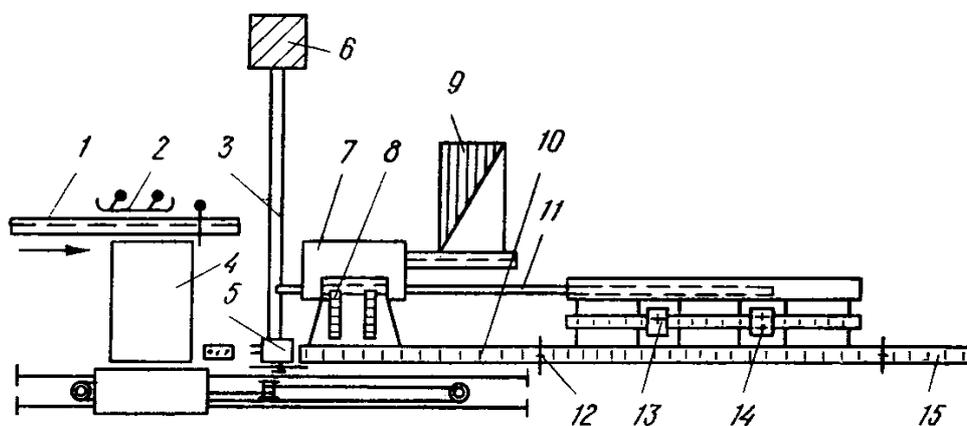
Технологическая схема одностаночного шпалорезного цеха: 1 – подающий лесотранспортер; 2 – автоматический сбрасыватель; 3, 11 – скребковые транспортеры для опилок и кусковых отходов; 4 – буферная площадка; 5 – шпалорезный станок ЦДТ-6-4; 6 – бункер; 7 – шпалооправочный станок ЛО-44А; 8 – поперечный питатель шпалооправочного станка; 9 – выносной лоток для окоренных шпал; 10 – рольганг; 12 – торцовочный станок ЦКБ-40-1; 13 – ребровый станок ЦР-4; 14 – обрезной станок Ц2Д-7А; 15 – выносной лесотранспортер для досок
